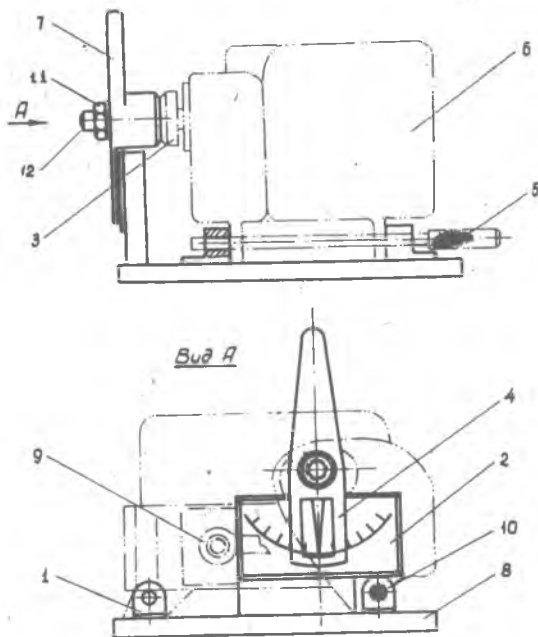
Рис. II. Приспособление для проверки угла поворота вала Р.М.
